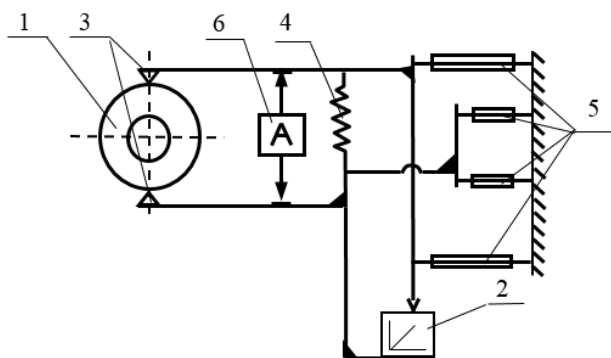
Вимірювальний пристрій для контролю зовнішнього діаметра деталі
